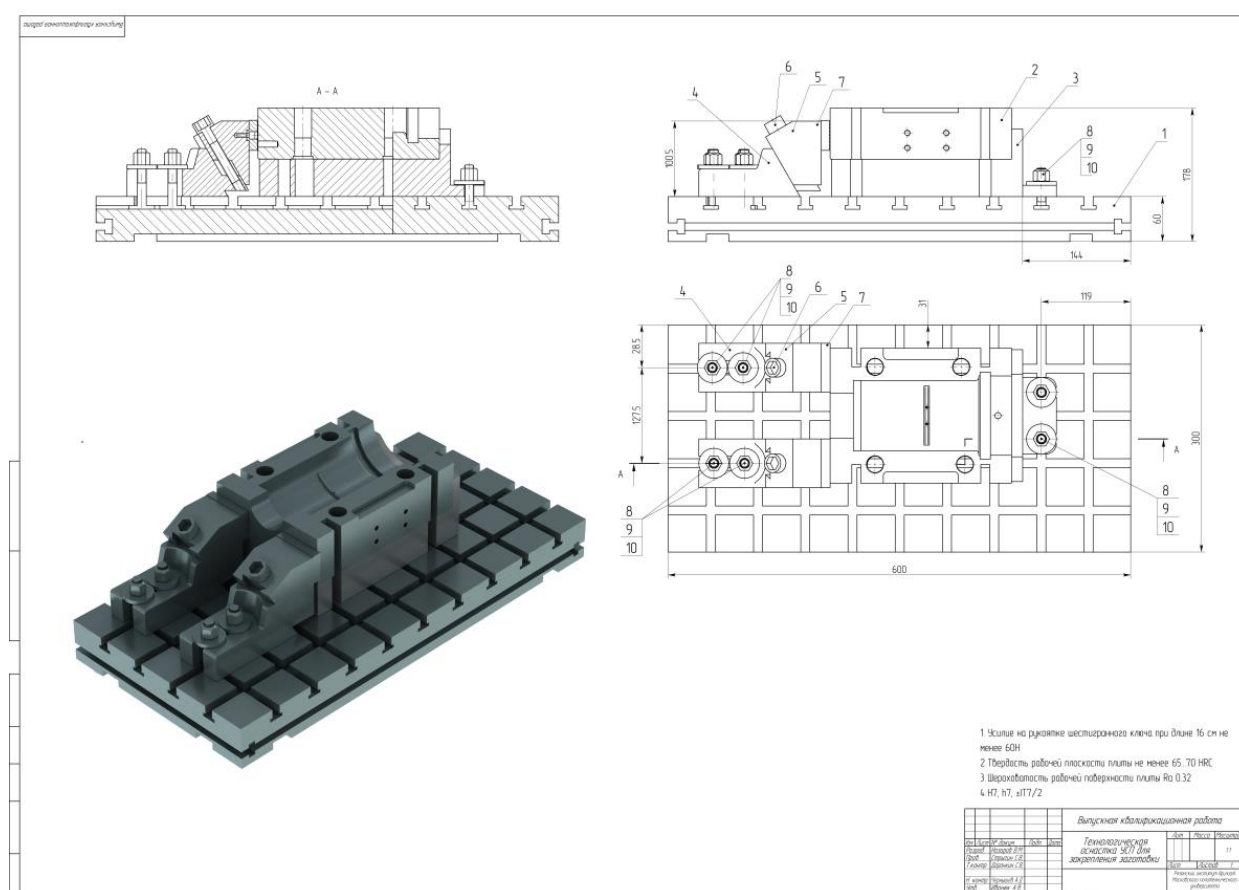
Чертеж приспособления с 3D моделью (предпочтительный)
